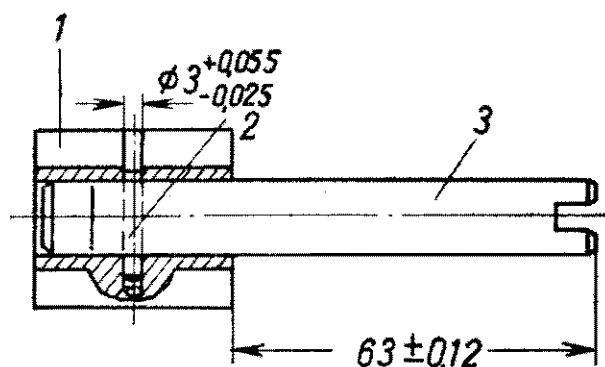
Крепление ведущей шестерни масляного насоса на валике:
